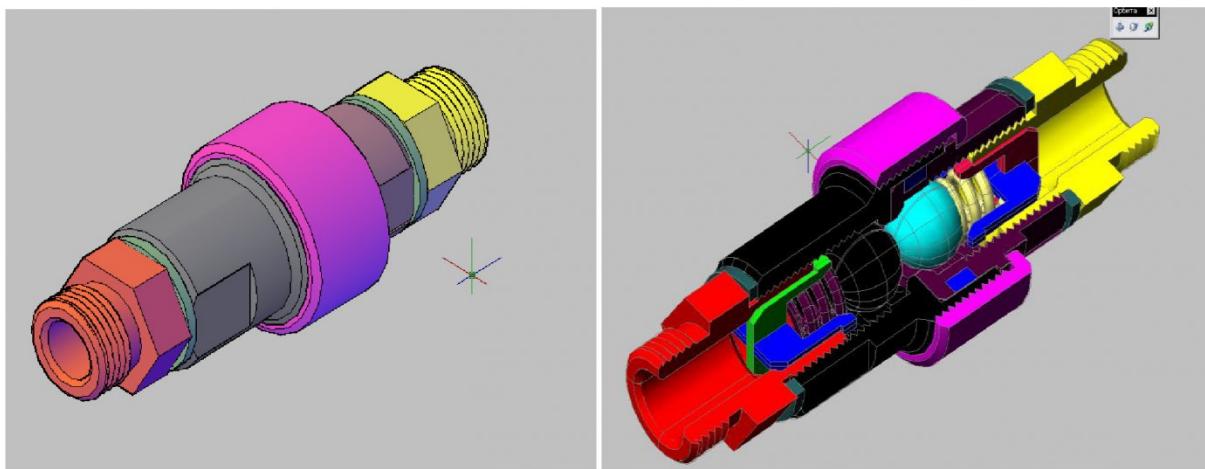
3D изображение запорного устройства с вырезом 1/4 сборочной единицы\
